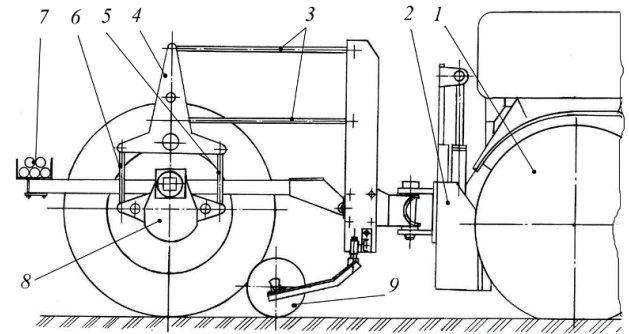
Шинный тестер [9-12]: 1 – тягач; 2 – привалочная рама; 3, 5, 6 – реактивные штанги; 4 – траверса; 7 – грузы; 8 – цилиндрический редуктор; 9 – путеизмерительное колесо
